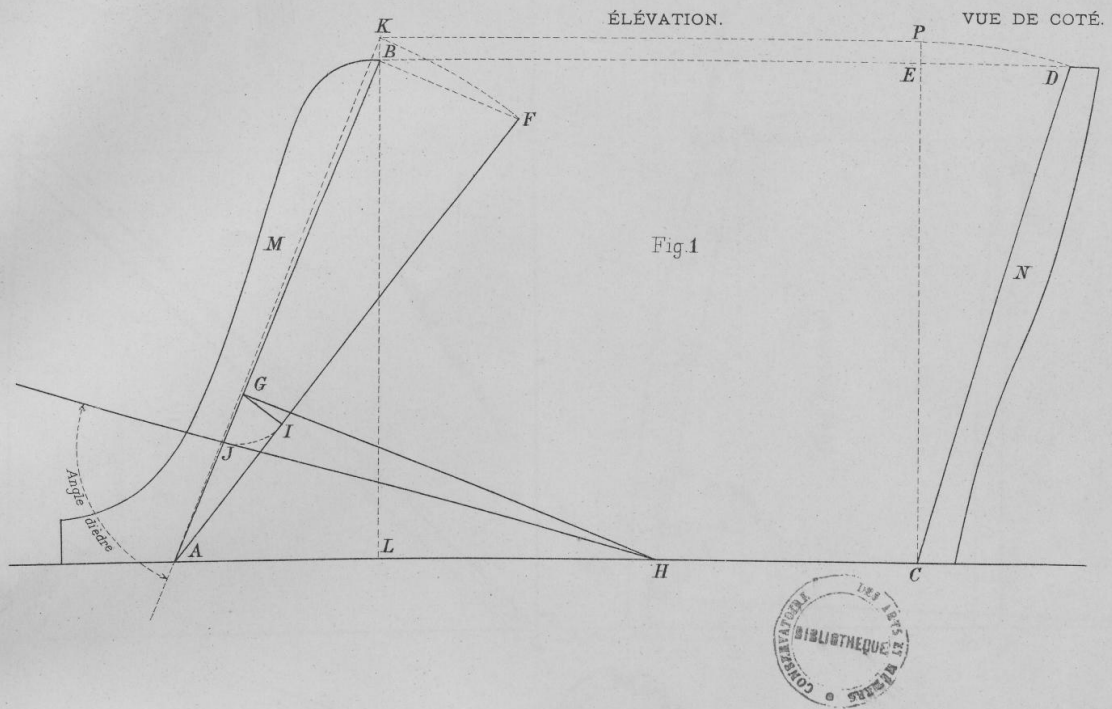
CONSTRUCTION DE L'ANGLE DIÈDRE EN PLAN HORIZONTAL ET RALLONGEMENT DU PIED DE PHAETON.
